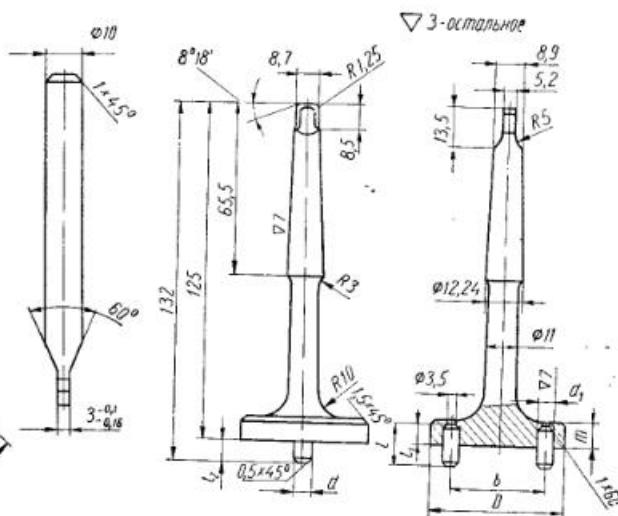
Шток для притирки клапанов двигателей типа NVD-36.
